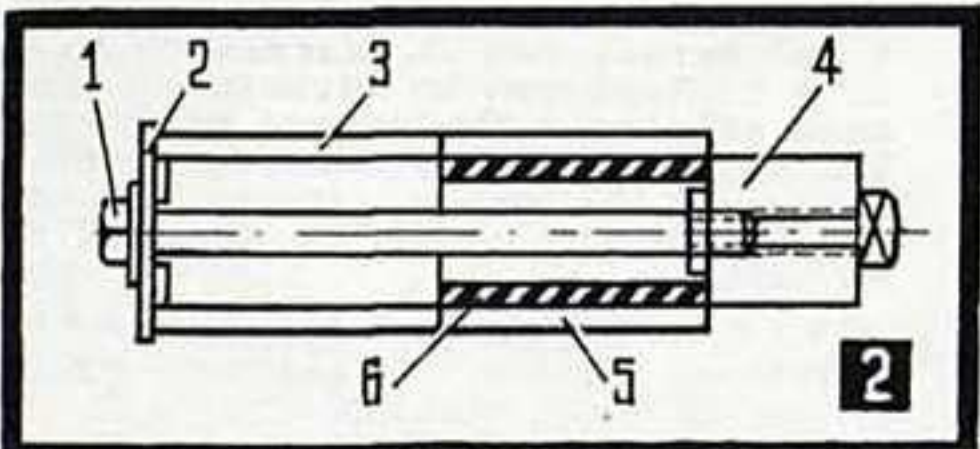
Приспособление в сборе: 1 — болт; 2 — шайба; 3 — трубка; 4 — гайка; 5 — кронштейн рессоры; 6 — втулка сайлент-блока.
